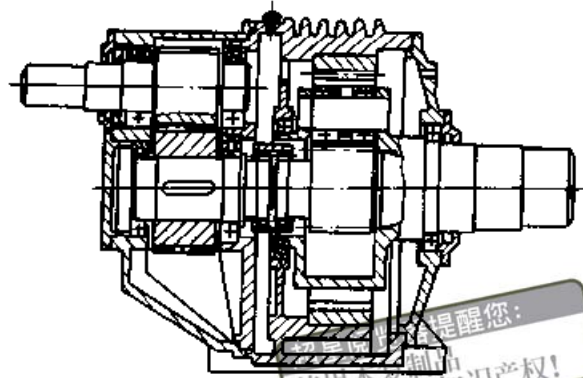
ZKP/ZZDP 单级派生系列行星齿轮减速器结构
